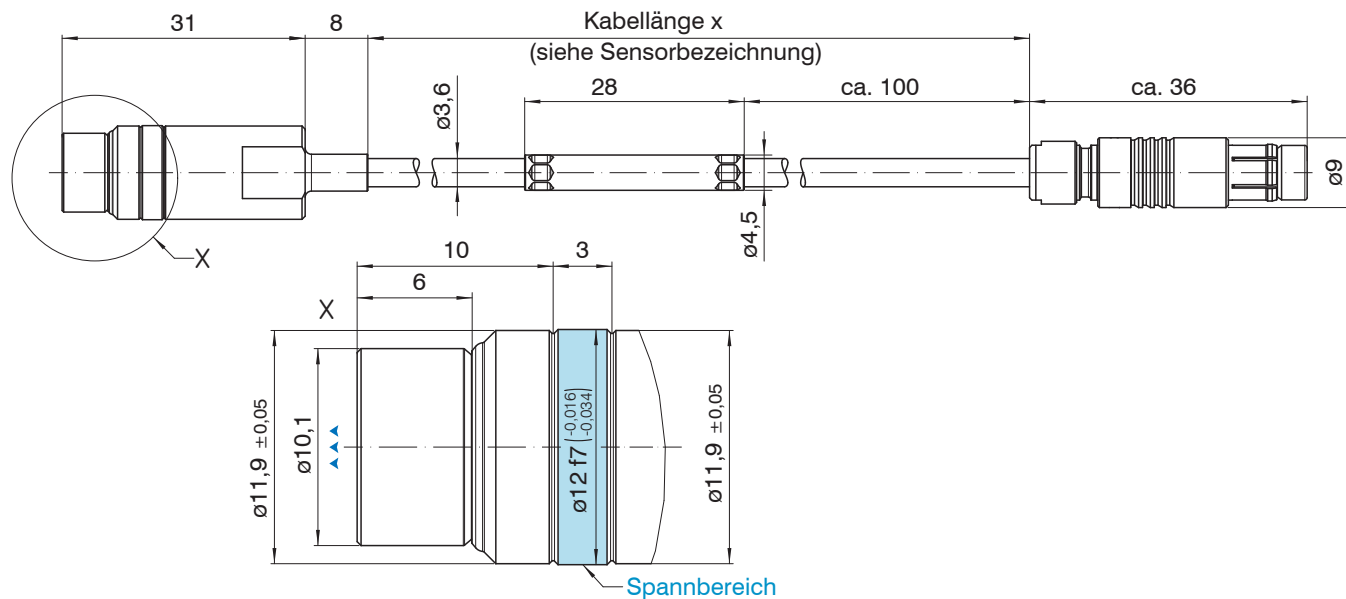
Maßzeichnung Sensoren ES-U3-T-CAx/mB0, Abmessung in mm
